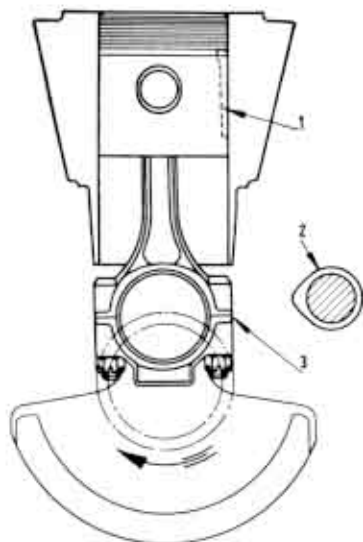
Modd. 500 L - 500 - 500 D e Nuova 500 Sport - Schema per il montaggio del complessivo biella-stantuffo sul motori.
